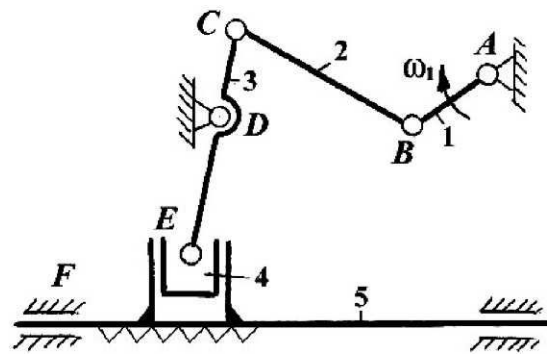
Механизм привода режущего аппарата фронтальной косилки
